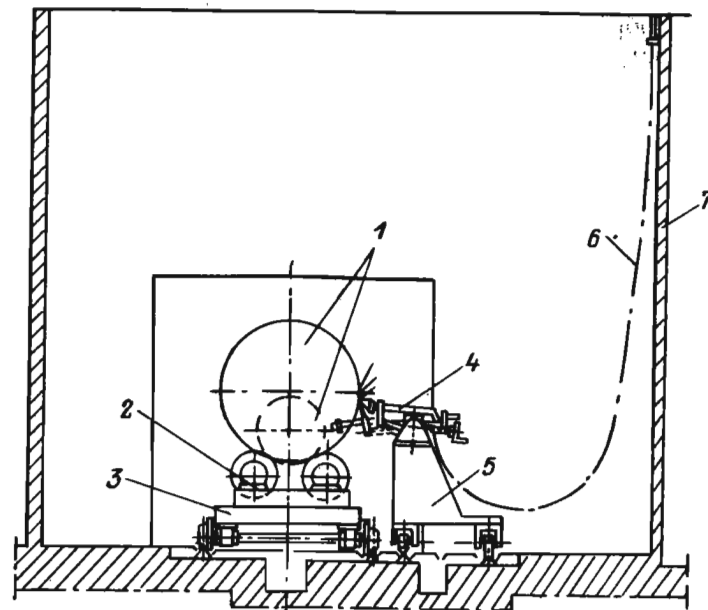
Схема установки для очистки вала струей воды высокого давления: 1 — обрабатываемый вал; 2 — опорные ролики; 3 — тележка; 4 — форсунка; 5 — камера; 6 — гибкий шланг; 7 — камера
